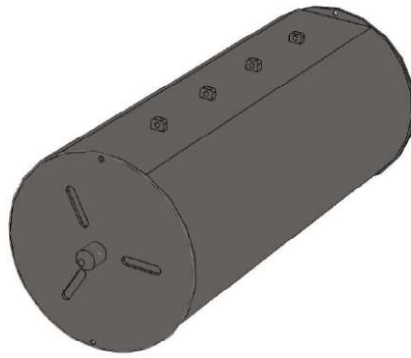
3D- модель внутрішнього циліндра барабана
